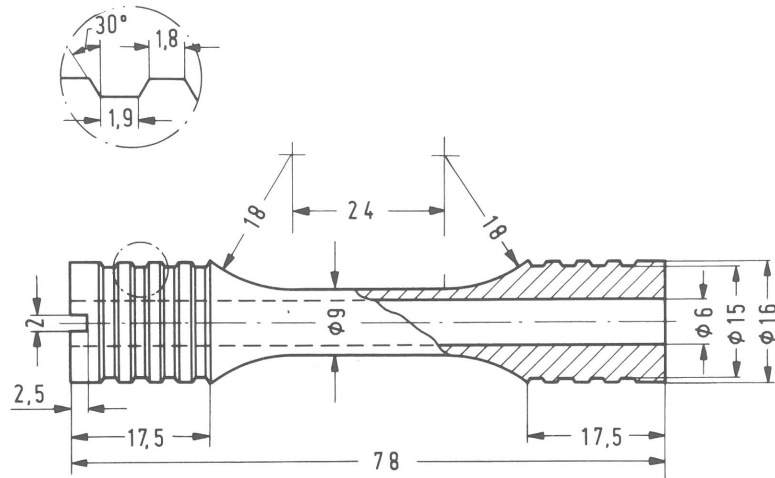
Hohlzylinderprobenkörper der Schwingfestigkeitsuntersuchungen.
